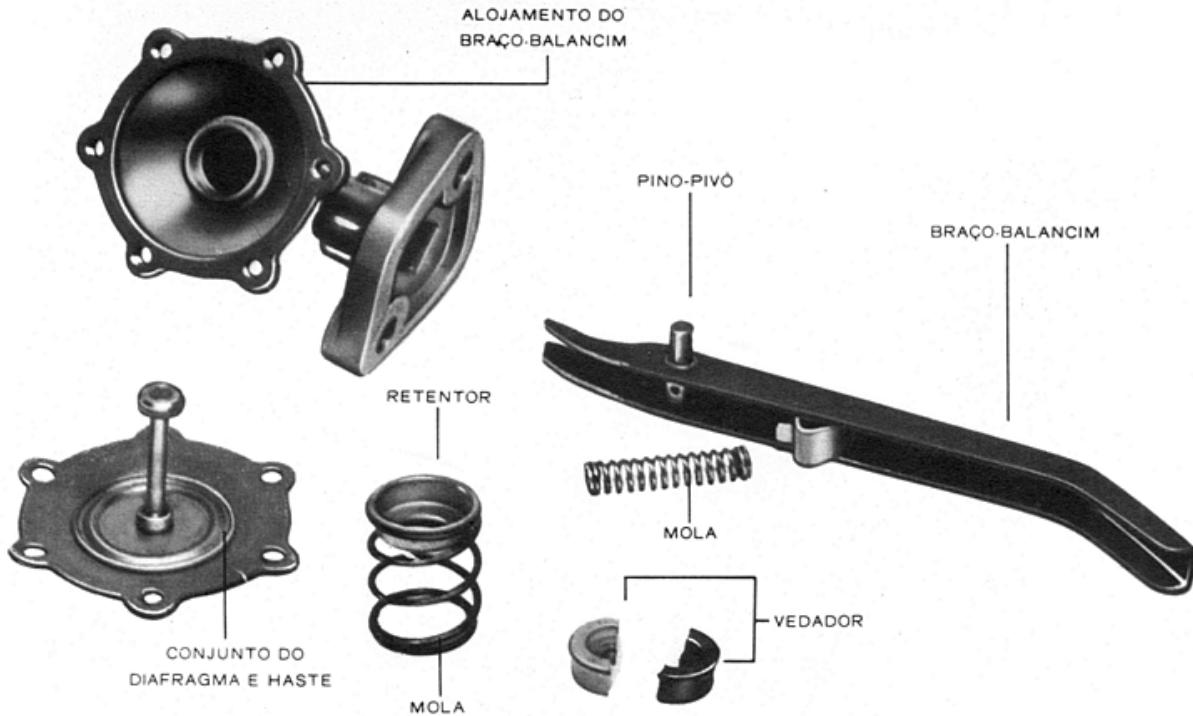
Desmontagem do corpo e conjunto do diafragma
